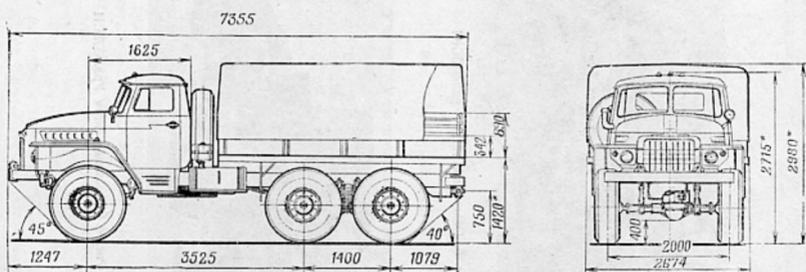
Габаритный чертеж автомобиля Урал-375Д
